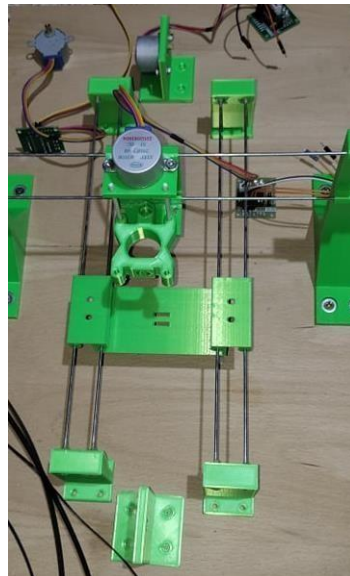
Début de l'assemblage de l'imprimante CNC.
